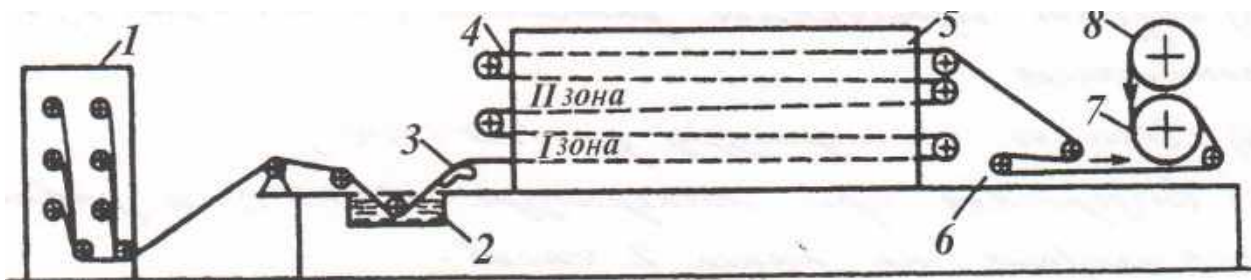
Схема установки типу УЛК: 1 – шпулярник; 2 – просочувальна ванна; 3 – віджимний пристрій; 4 – вуглецева стрічка; 5 – сушильна камера; 6 – механізм протягування; 7 – механізм намотування; 8 – фторопластова підкладка
